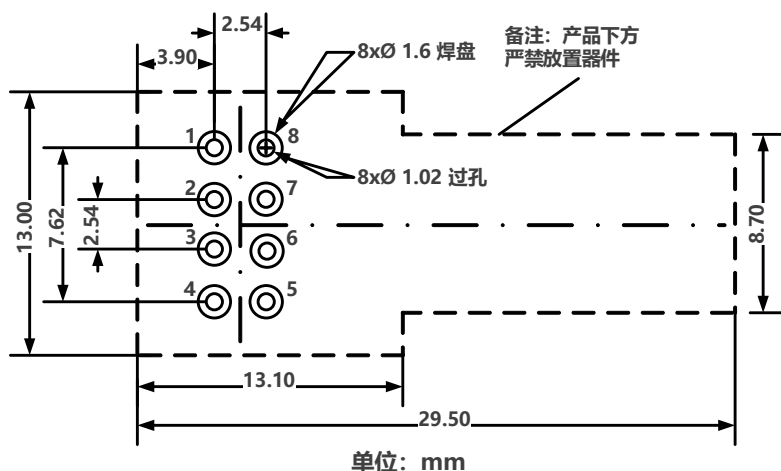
PCB Layout 设计推荐尺寸图（俯视图）
